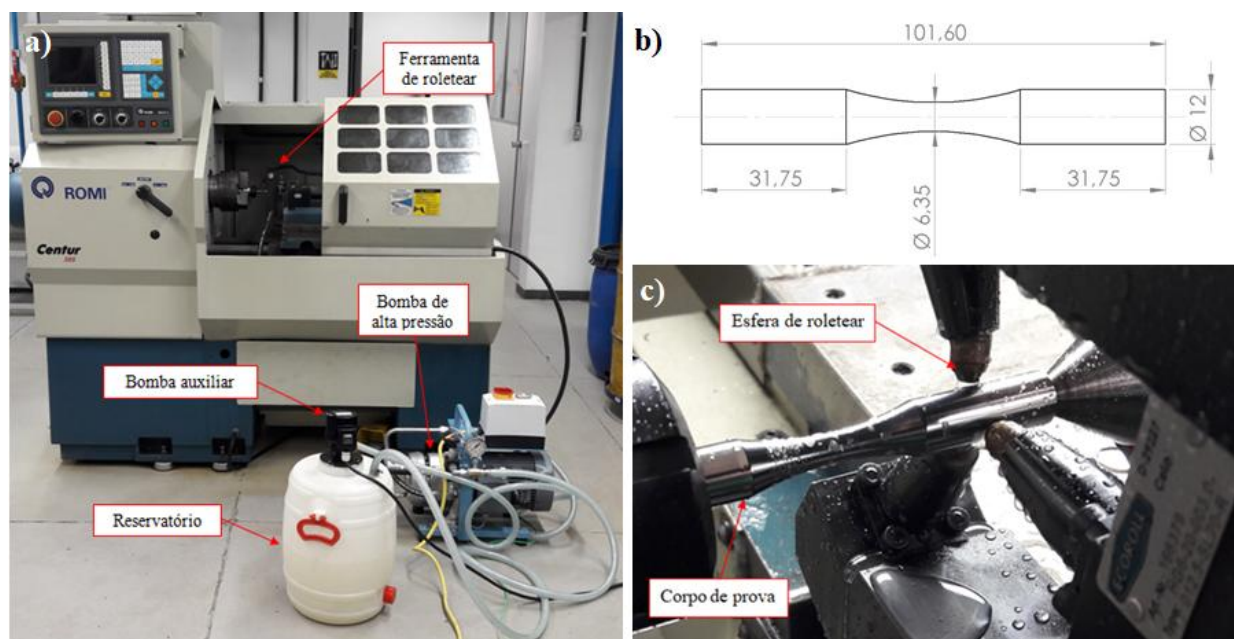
a) Montagem do equipamento de roletear no torno, b) dimensões do corpo de prova (em mm) e c) ferramenta de roletear acoplada à torre do torno.
